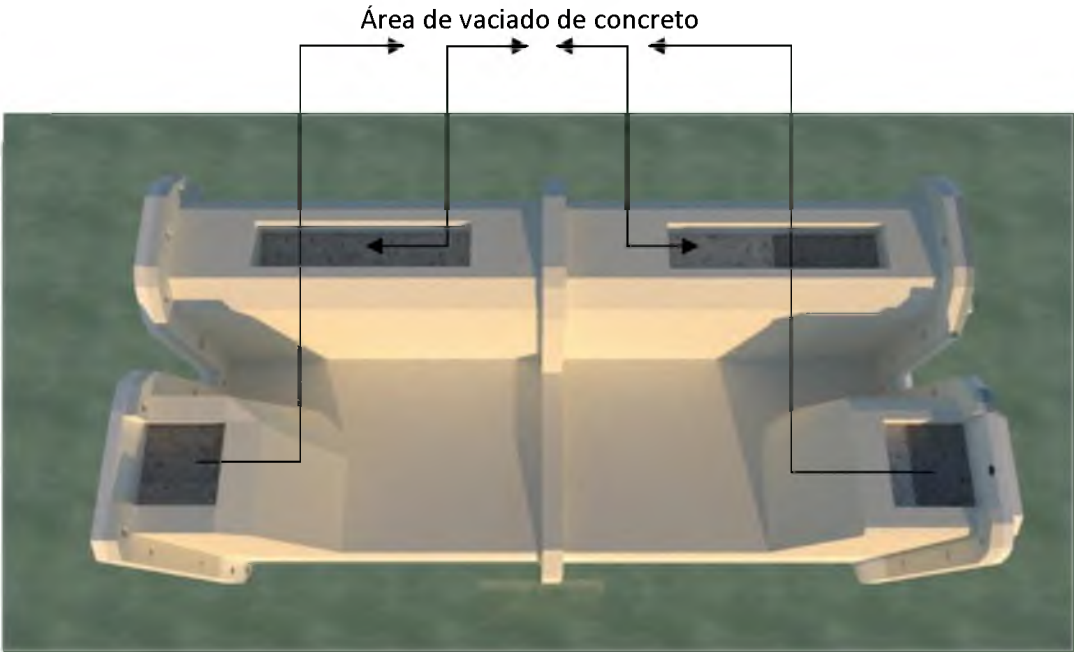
Molde del asiento dos piezas juntas. V. Inferior
